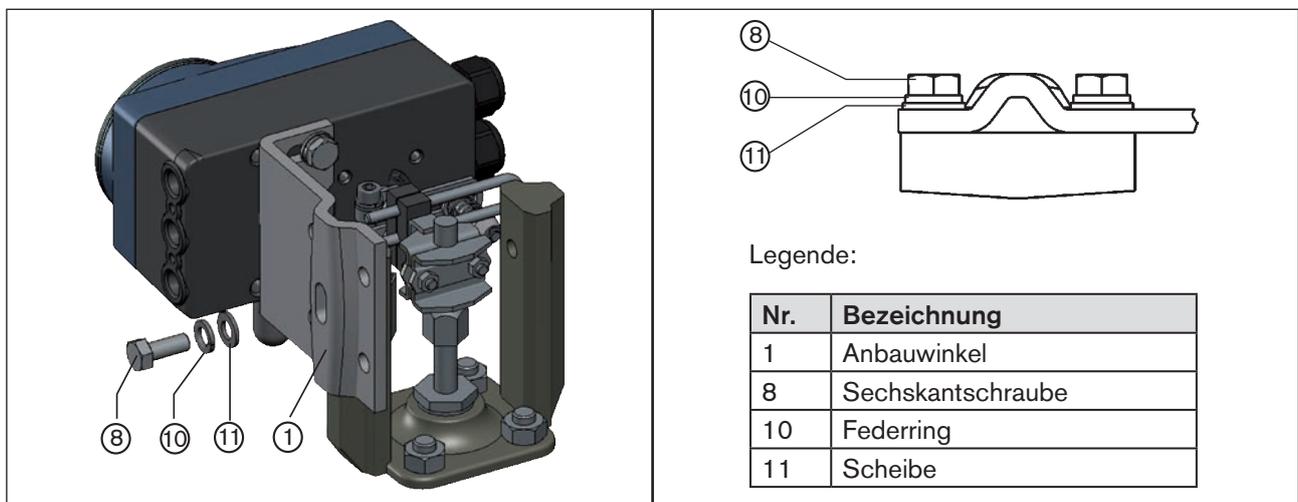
Positioner mit Anbauwinkel befestigen; bei Antrieben mit Gussrahmen
